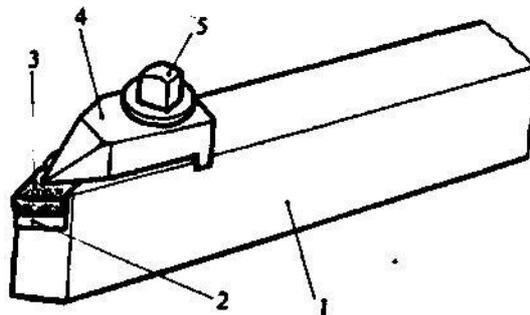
Резьбовой резец с механическим креплением ромбической пластинки 1- державка; 2- опорная пластинка; 3- режущая пластинка; 4- прижимная планка; 5- винт
